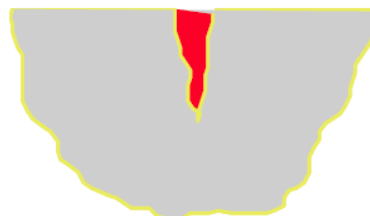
Remoção do excesso de LP da superfície [9]
